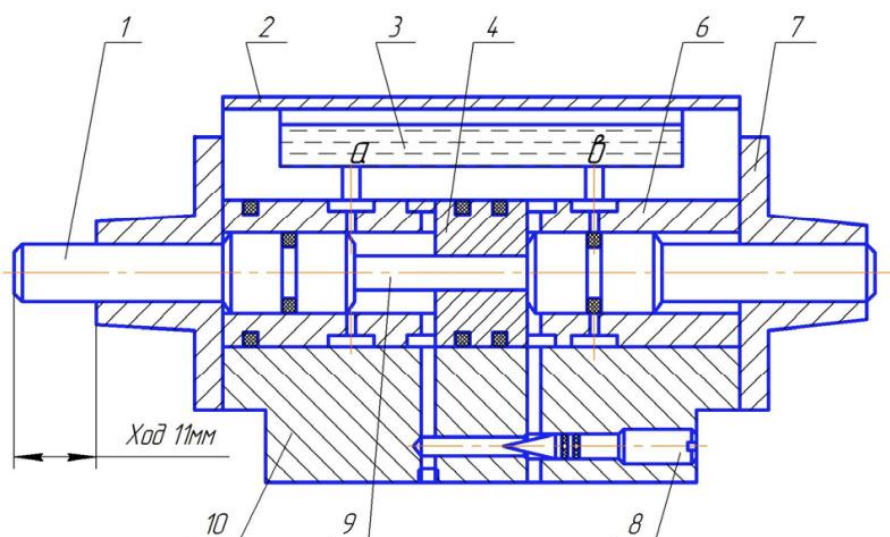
Гідравлічний амортизатор кута поворота руки: 1 – шток; 2 – кришка; 3 – мастило (І-20А); 8 – голка дросельна; 10 – корпус.
